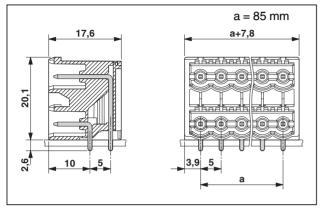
Abmessungen CCDN 2,5/18-G1 P26 THR
